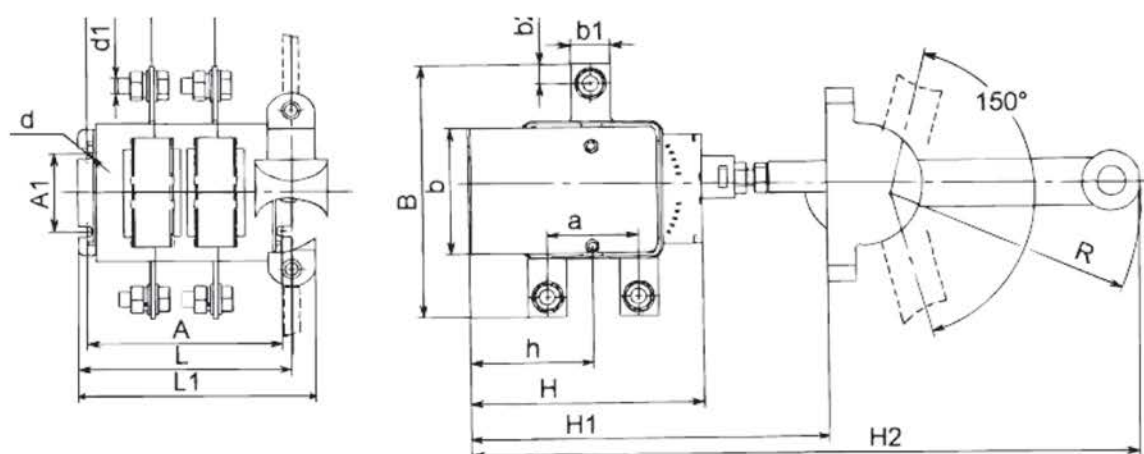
Выключатель-разъединитель двухполюсный на два направления с боковой рукояткой.
